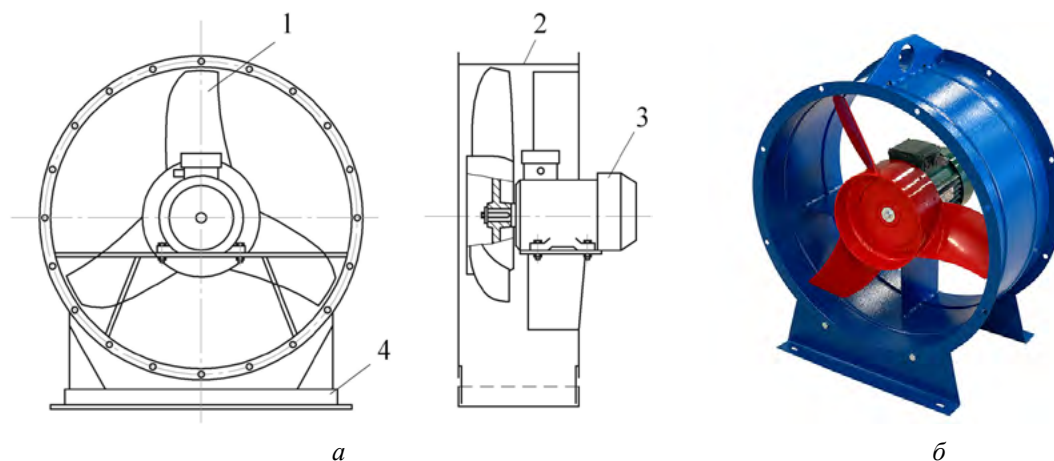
Схема (а) и вид (б) осевого вентилятора: 1 — лопатки и рабочее колесо вентилятора; 2 — кожух вентилятора; 3 — электродвигатель; 4 — крепления с виброопорами
